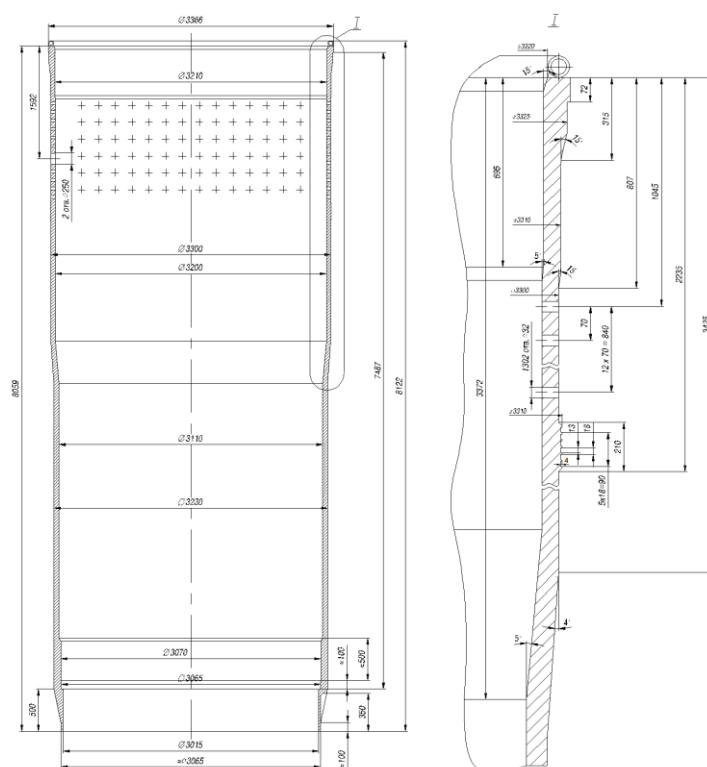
Общий вид шахты реактора ВВЭР-440 с кольцевым уплотнителем
